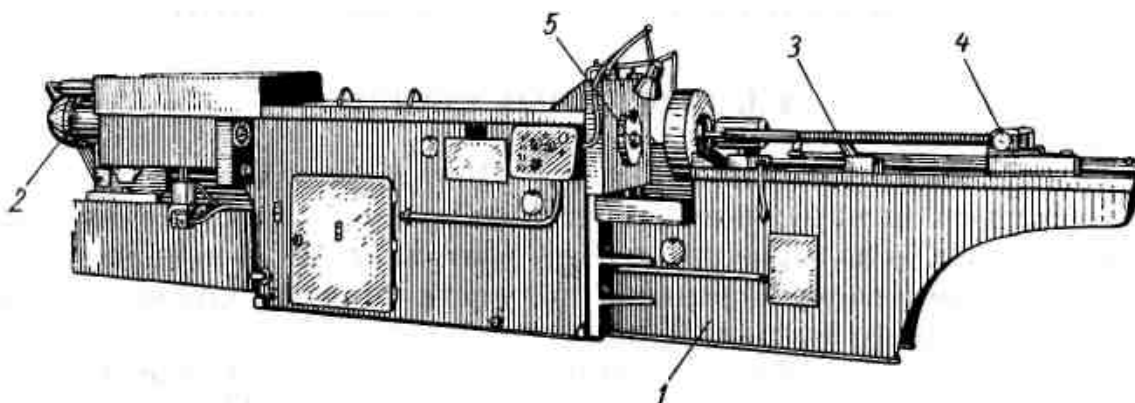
Типовая компоновка горизонтально-протяжного станка
